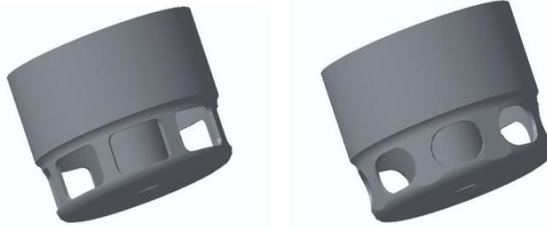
Форми отворів на твірній поверхні циліндра резонатора
